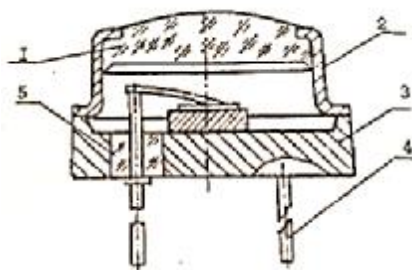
Фоторезистор: 1 – скляне віконце; 2 – кришка; 3 – корпус; 4 – вивід; 5 – бусинка
